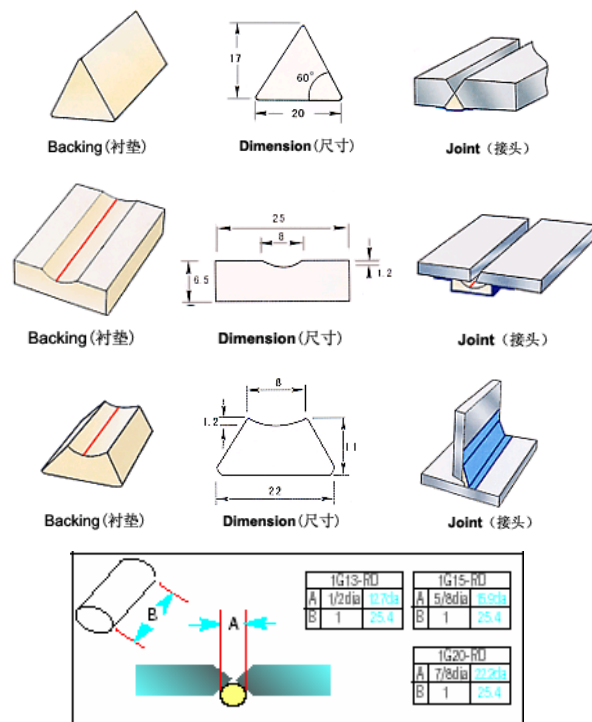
Suportes cerâmicos. (Xiangshan Welding Backing Factory e Gullco Internacional, 2006)
